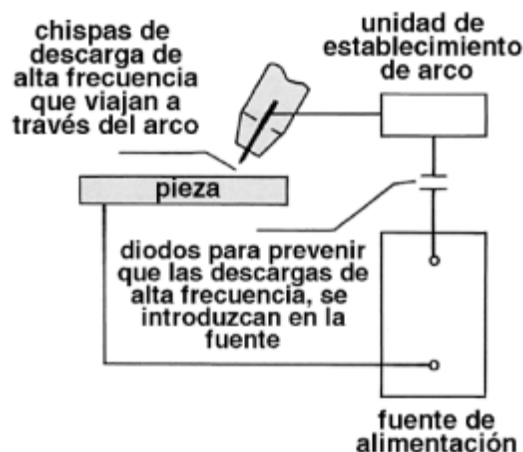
Corriente alterna soldadura TIG.
